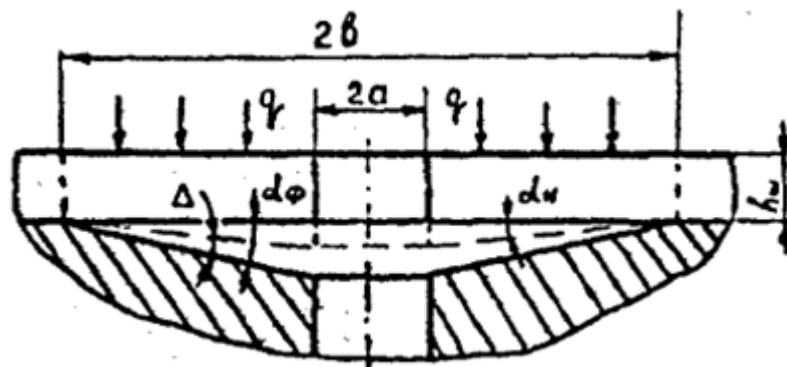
Схема для розрахунку конструктивних параметрів опорної поверхні склянки форсунки
